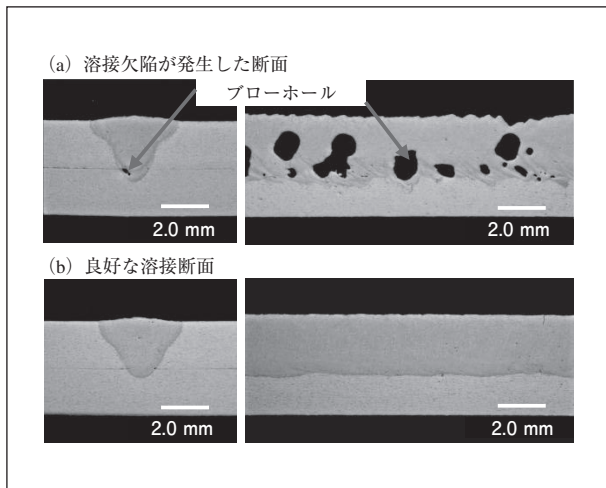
2 mm厚の6000系アルミニウム合金の重ね溶接断面
